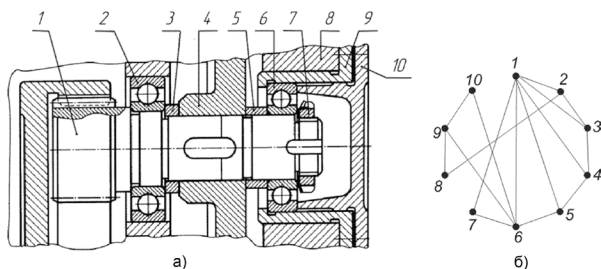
Вал цилиндрического редуктора (а), граф связей конструкции (б)
